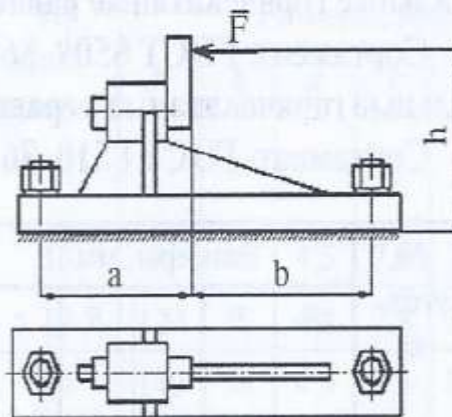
Схема к расчету болтов, крепящих стойку к бетонному основанию
